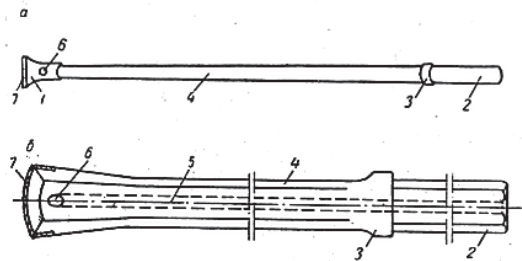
Буровий інструмент: а – складний бур; б – цільний бур; 1 – знімна бурова головка; 2 – хвостовик; 3 – буртик; 4 – штанга; 5 – осьовий канал; 6 – отвір для промивання; 7 – пластинка твердого сплаву
